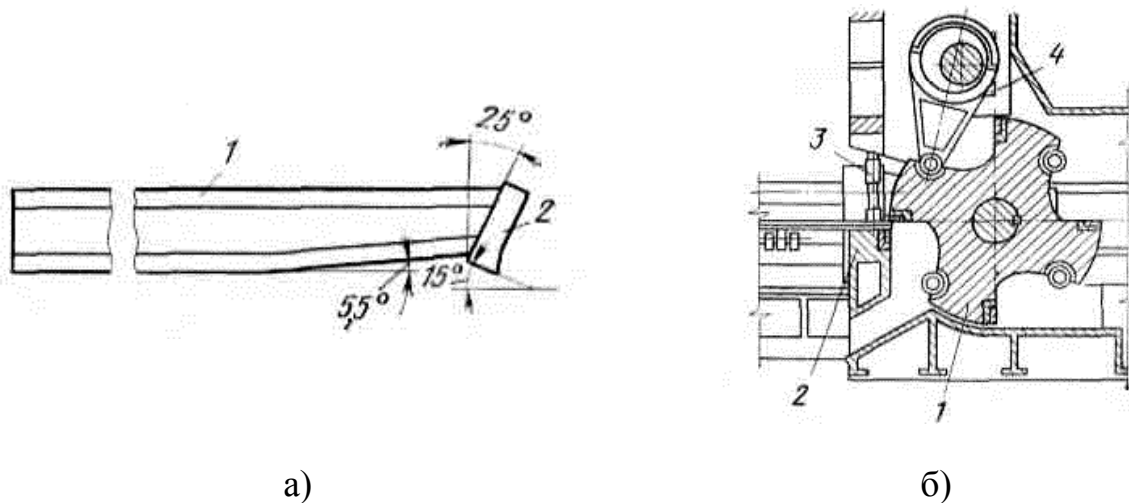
Здвоєні кромкообрізні ножиці: а – форма ножа; б – конструктивна схема
